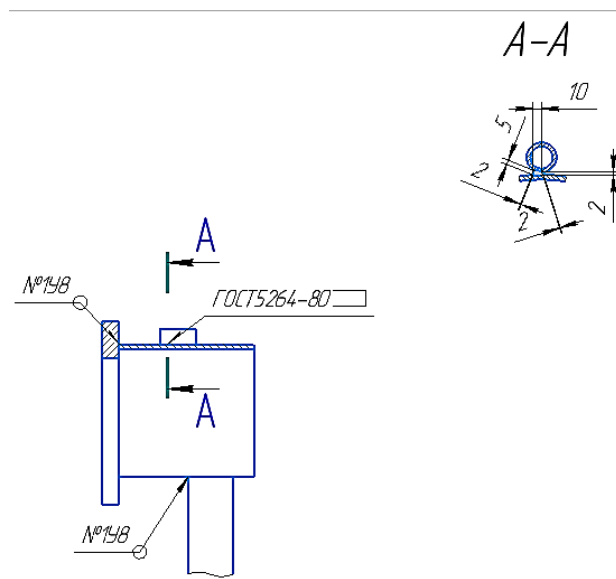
Оформление на чертеже формы и размеров нестандартного шва с помощью сечения
